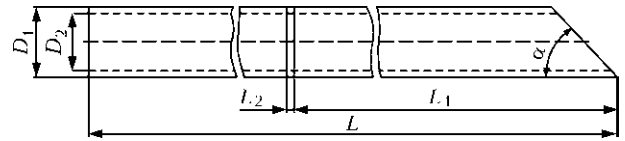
Схема модельного образца полимерной трубы, сваренного с использованием процесса стыковой сварки
